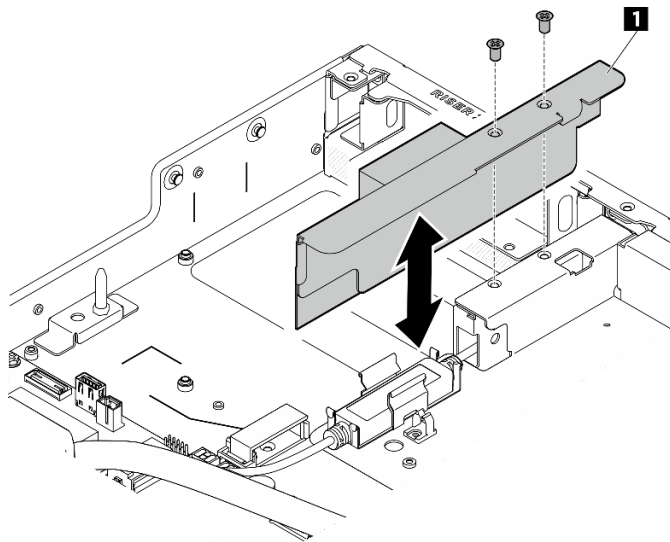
Entfernen der DPU-Luftführung und der Halterungsbaugruppe
